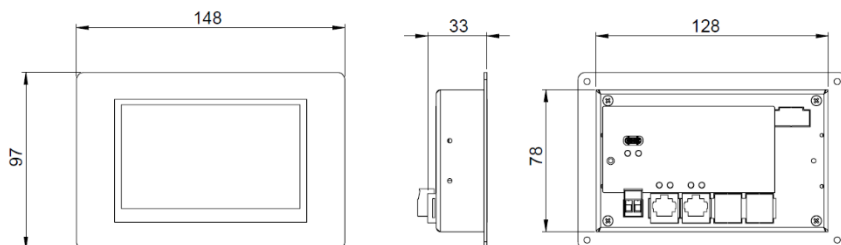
Dimensões do Equipamento MASTERVIEW 4”.
